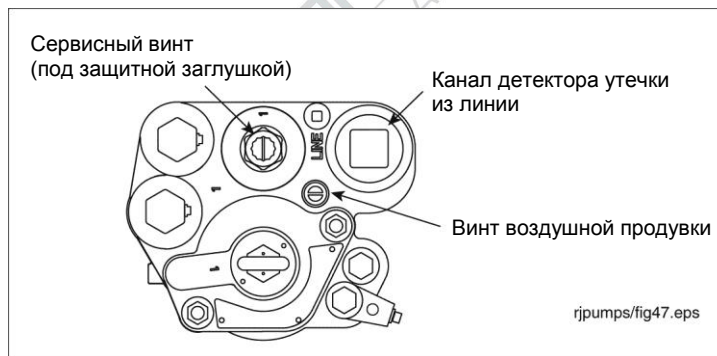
Местоположение заглушки выпускного канала для датчика утечки из линии
